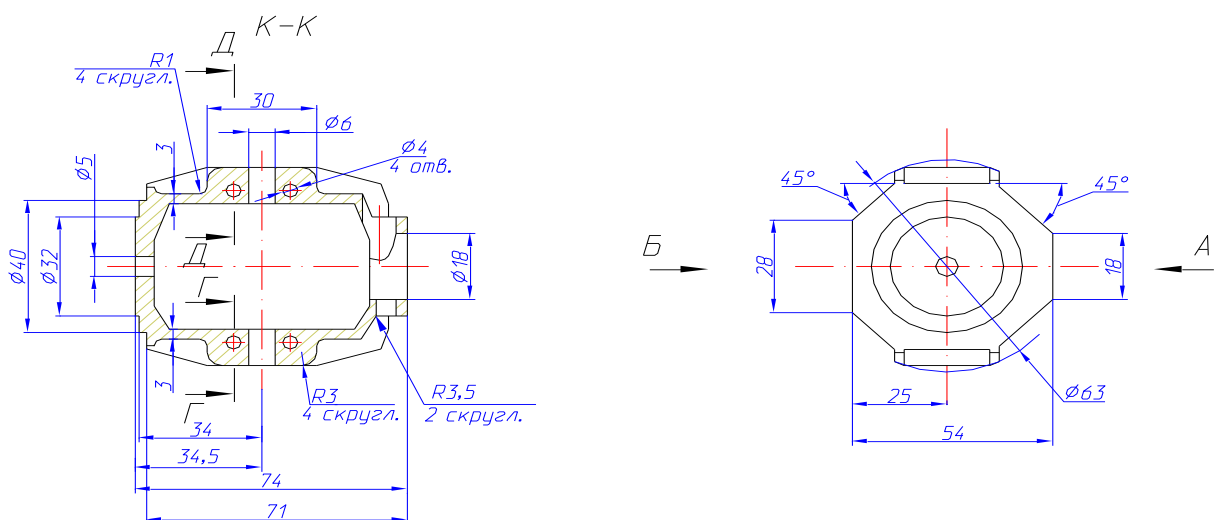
Ескіз заготовки „Корпус гіромотора”.
